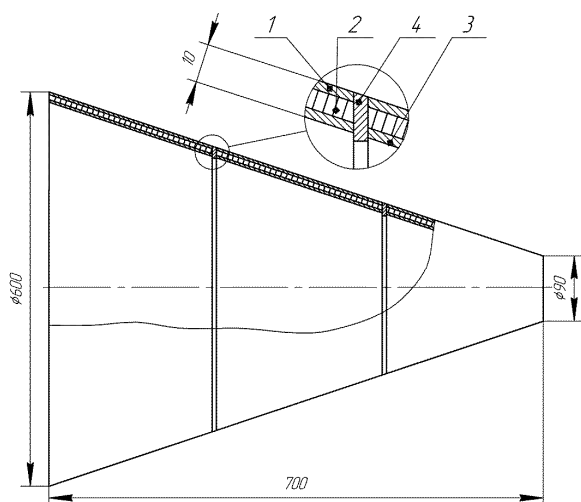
Схема конструкции конуса стекателя двигателя с однослойным заполнителем:
